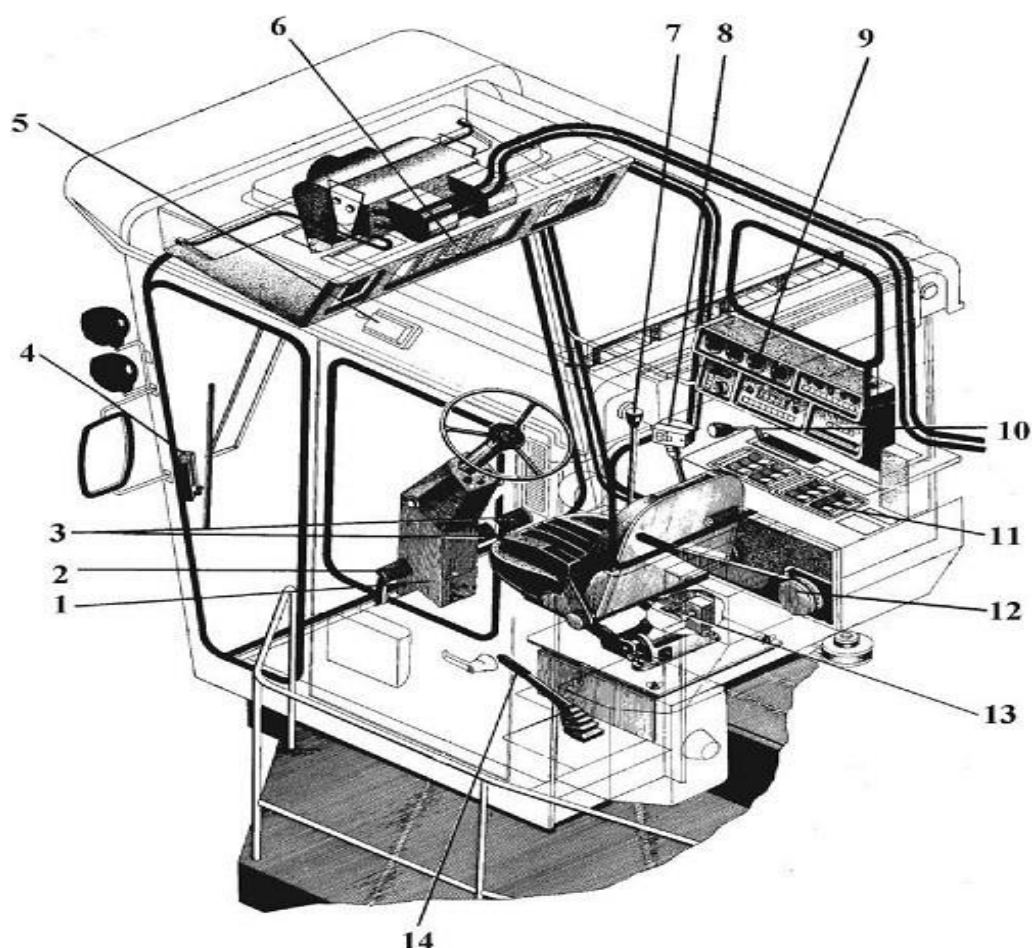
1-рулевая колонка; 2-педаль блокировки коробки диапазонов; 3-педали тормозов; 4-блок индикации потерь; 5-плафон; 6-верхняя панель приборов; 7-рычаг управления коробкой диапазонов; 8-рукоятка управления ГСТ; 9-щиток приборов; 10-рычаг управления подачей топлива и остановом двигателя; 11-пульт управления; 12-рычаг управления подбарабаньем; 13-педаль сброса подбарабанья; 14-рычаг стояночного тормоза.
